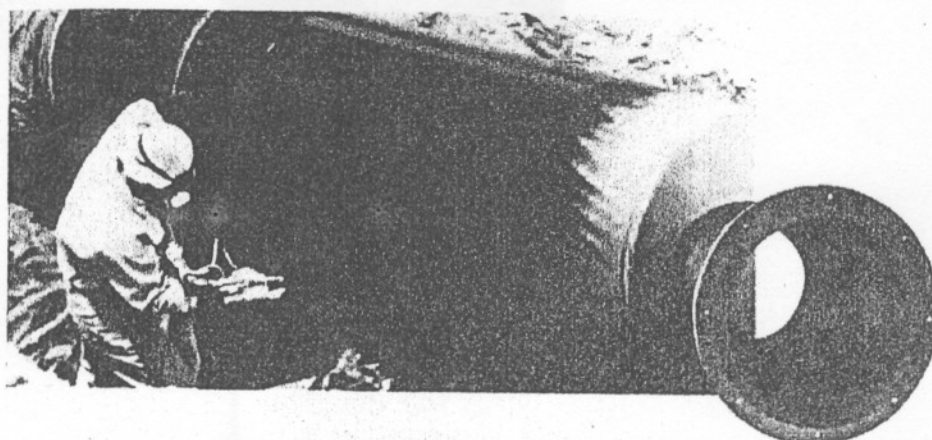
REVESTIMIENTO DE TUBERÍAS INTERNA Y EXTERNAMENTE
